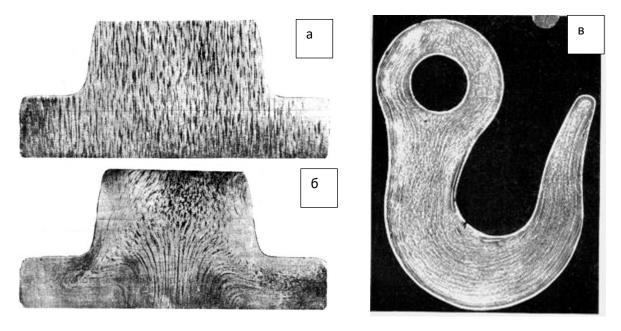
Макроструктура заготовок деталей, изготовленных: а) обработкой резанием; б) штамповкой; в) ковкой
